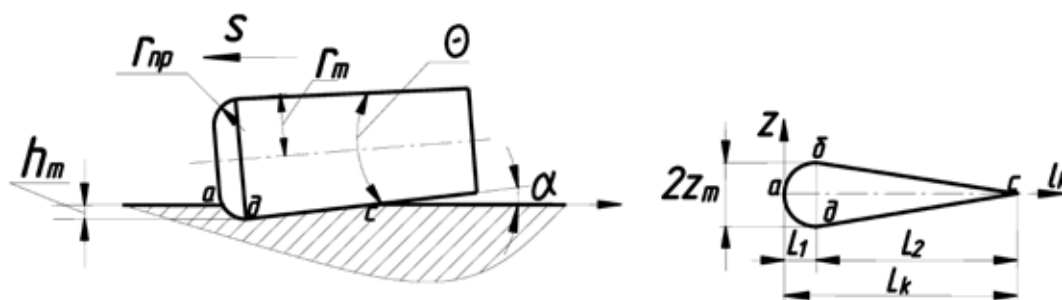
Внедрение ролика в поверхность детали при обработке поверхностным пластическим деформированием (а) и форма и размеры каплевидного контакта, образуемого при обработке цилиндрических поверхностей коническими роликами (б)
